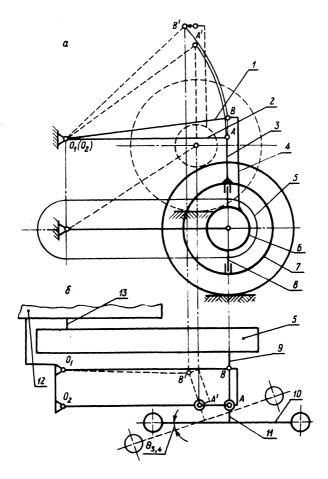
Кинематика механизма автоматического поворота задних колес крутосклонного трактора: а — вид сбоку; б — вид сверху.
